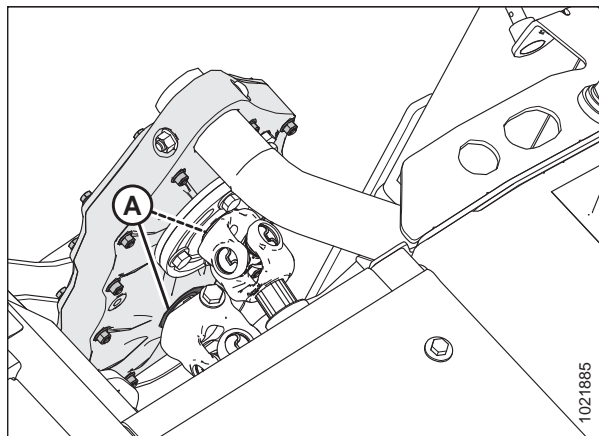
Подшипники редуктора синхронизации вальцов
